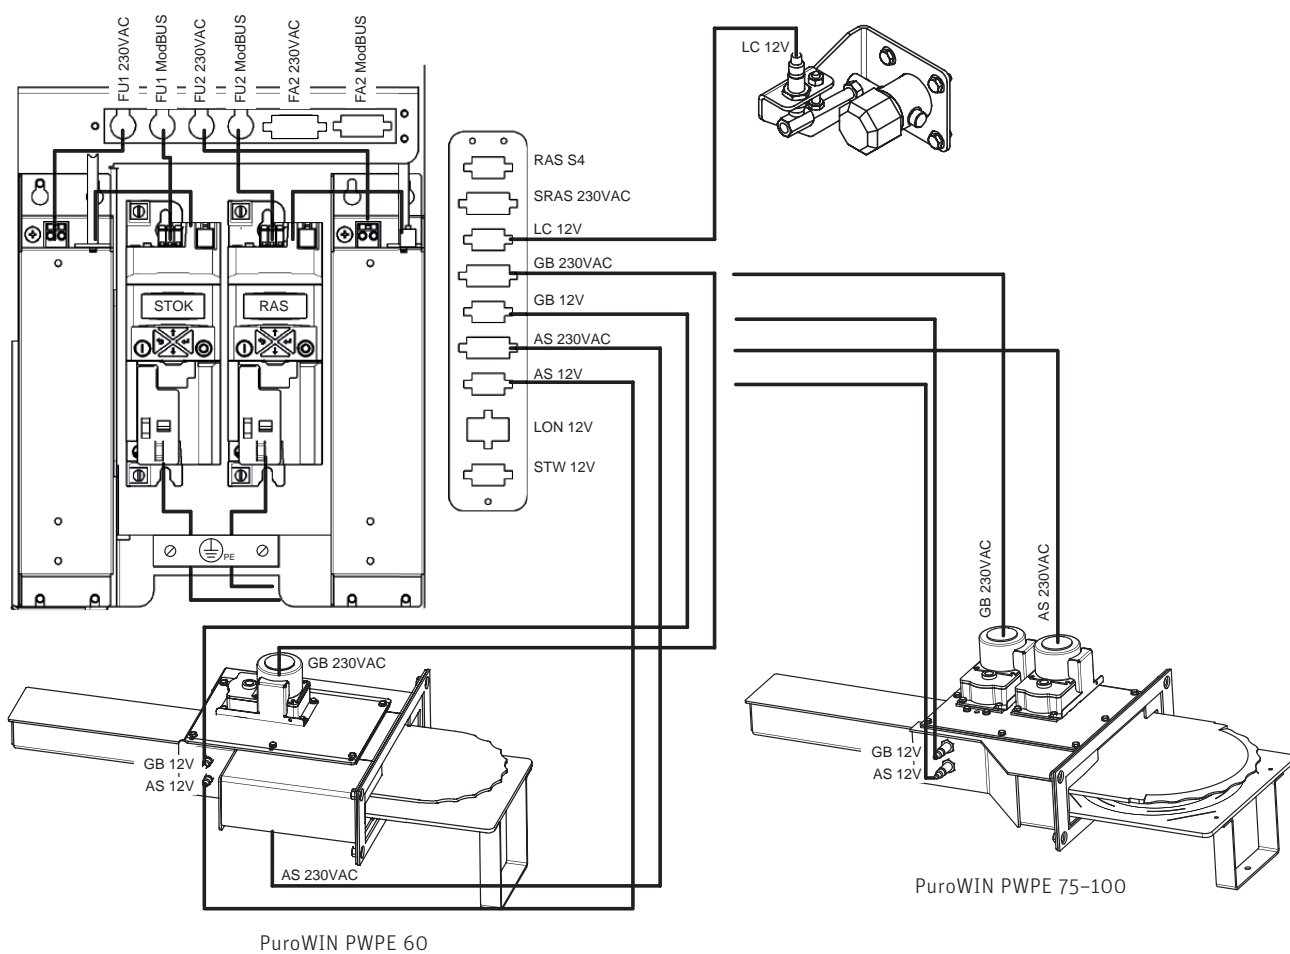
Inserire 3 interruttori di prossimità e 2 motori
